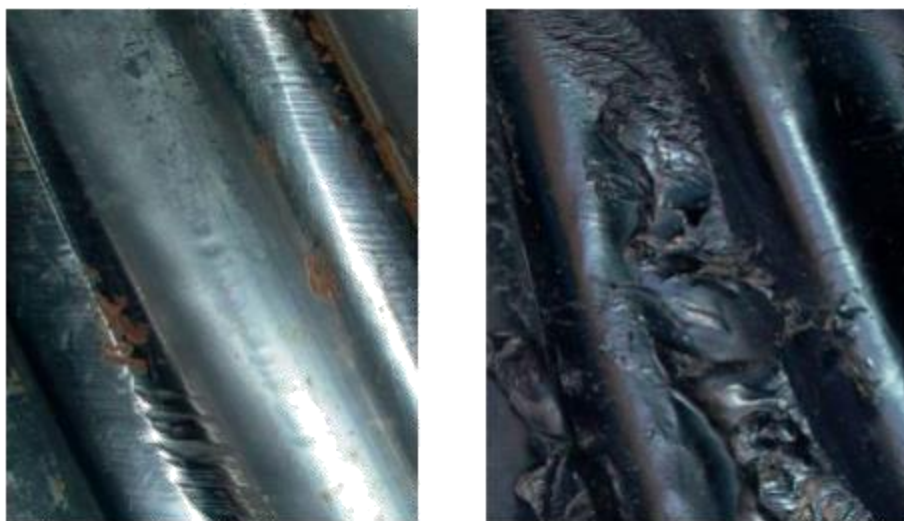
Износ поверхностей ротора и статора винтового забойного двигателя: а – износ поверхности ротора; б – износ поверхности статора
